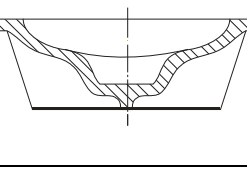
Примеры крепления знаковых частей на моделях отливки
